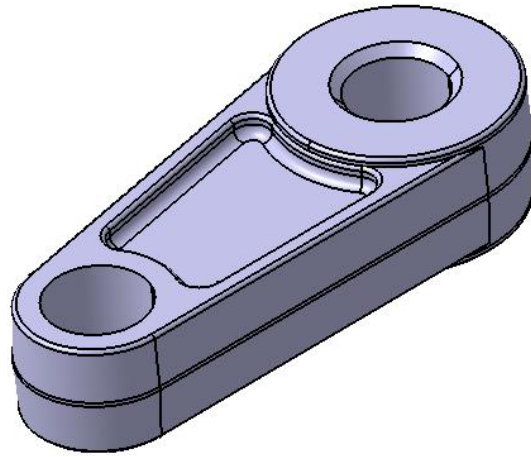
Získání negativního tvaru v CAD za použití Booleovské operace odčítání [105]
